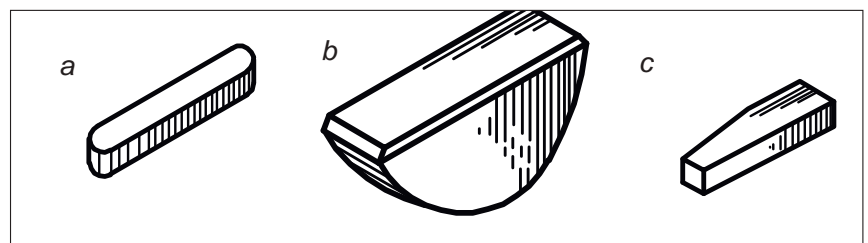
Tipuri de pene: a – pană paralelă cu capete rotunde; b – pană-disc; c – pană înclinată
